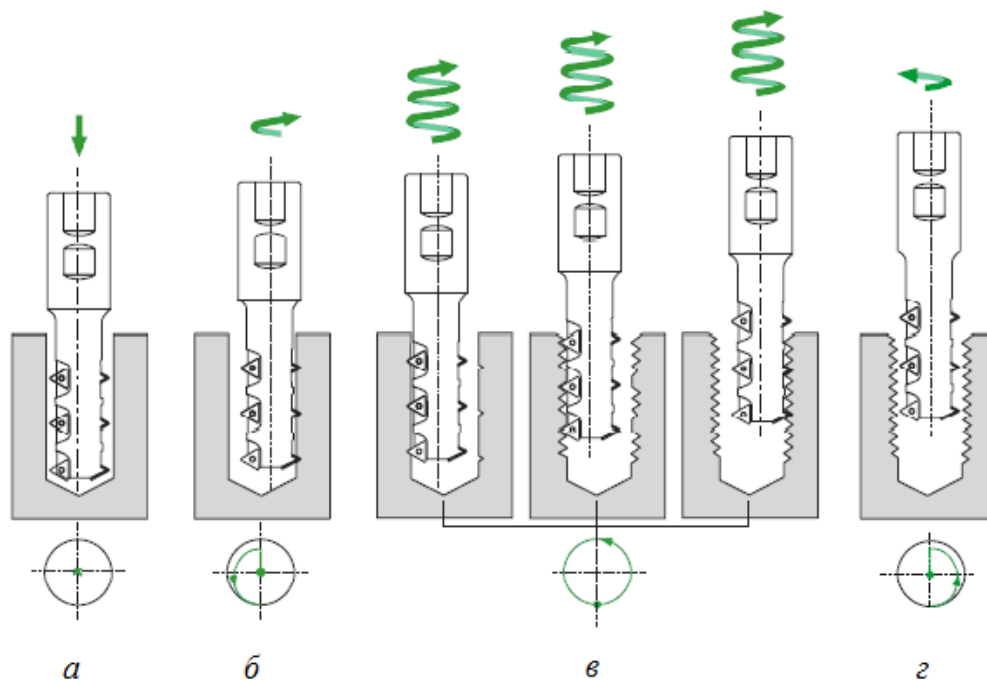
Кинематическая схема процесса обработки фрезой с шахматным расположением резьбовых профилей [11]
